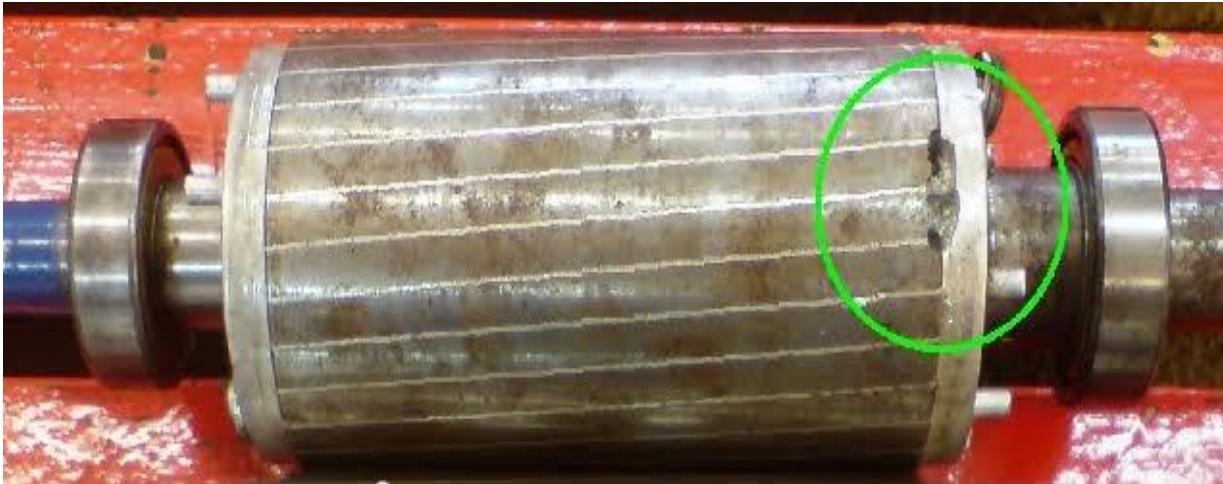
Rotor à cage d'écoreuil avec défauts.
